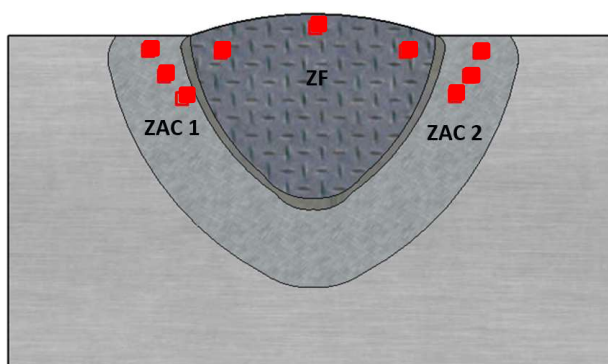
Zonas de interés de la soldadura donde se realizaron las indentaciones.
